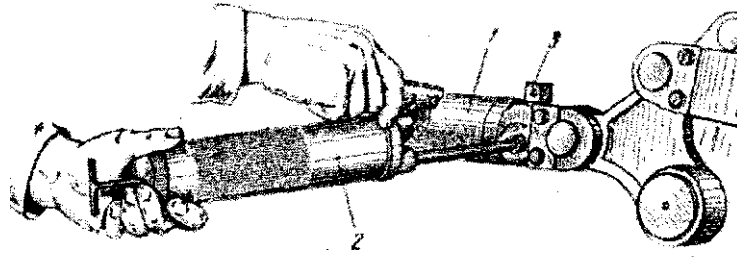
Натягнення гусеничного ланцюга 1 - циліндр гідронатягувача; 2 - шприц важільно-плунжерний; 3 - корпус клапана
